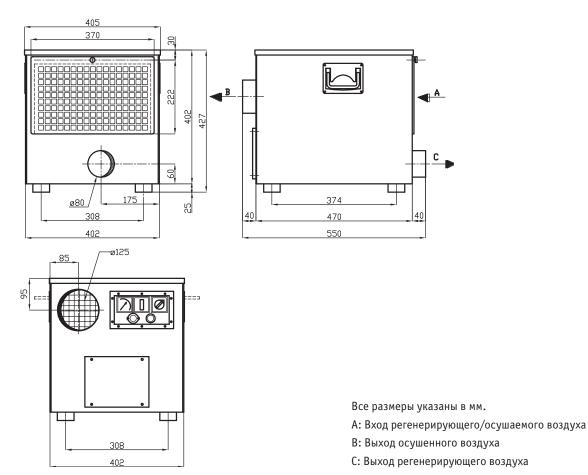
Габаритный чертеж осушителя AD 290 B.
